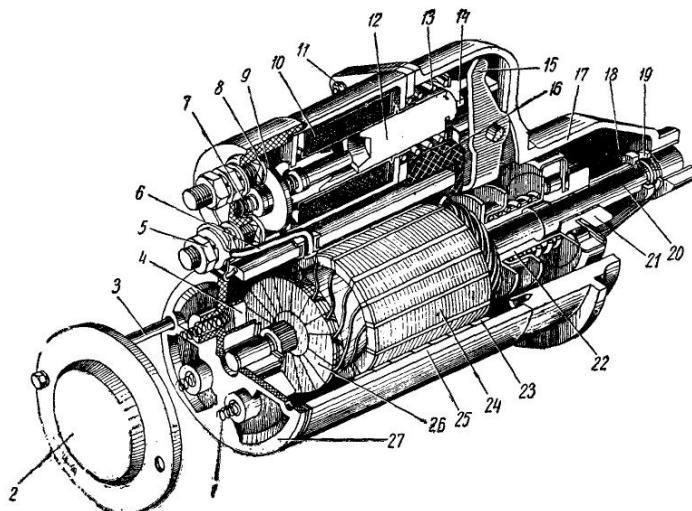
Стартер СТ 362: 1 – пружина щетки; 2 – колпак; 3 – болт стяжной; 4 – щетка; 5 – гайка; 6 – перемычка; 7, 13 – пружины возвратные; 8 – контакт; 9 – диск контактный; 10 – катушка тягового реле; 11 – винт; 12 – якорь тягового реле; 14 – серьги; 15 – рычаг включения стартера; 16 – прокладка уплотнительная; 17 – крышка со стороны привода; 18 – кольцо; 19 – шайба; 20 – вал якоря; 21 – шестерня включения; 22 – привод стартера; 23 – обмотка возбуждения электромагнита; 24 – якорь стартера; 25 – корпус стартера; 26 – коллектор; 27 – крышка со стороны коллектора.
